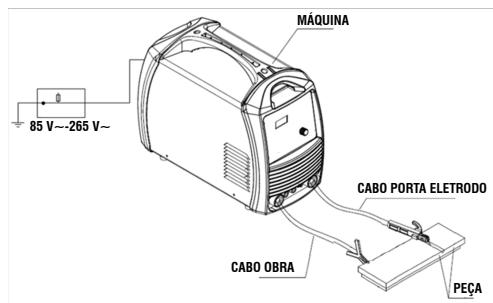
Montagem dos cabos de solda para soldagem de Eletrodo Revestido (MMA)
